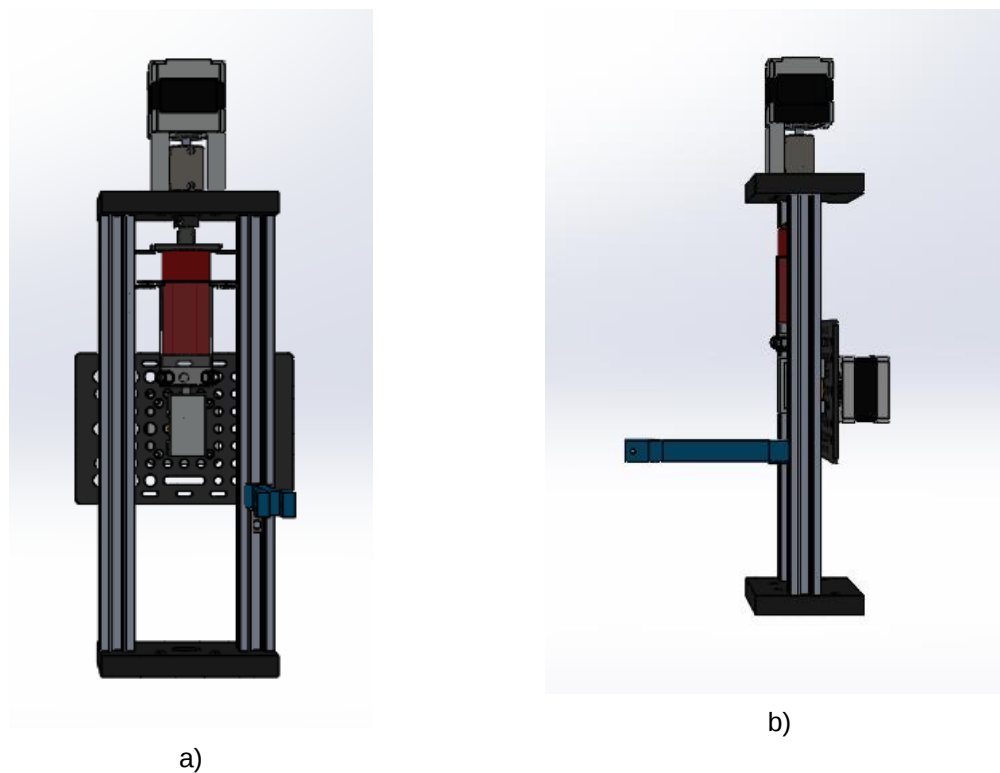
Diseño de la máquina para el llenado de viales. a) Vista frontal, b) Vista lateral.
